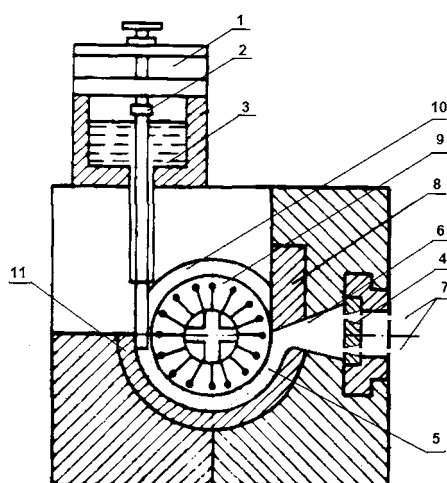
Схема процесса непрерывного прессования Конформ-Кастэкс полых профилей из жидкого металла. 1 – литейный желоб; 2 – устройство регулирования расхода жидкого металла; 3 – жидкий металл; 4 – матрица; 5 – фронт кристаллизации; 6 – камера сварки; 7 – полые профили; 8 – упор; 9 – колесо; 10 – кольцевая канавка; 11 – кольцевая вставка
